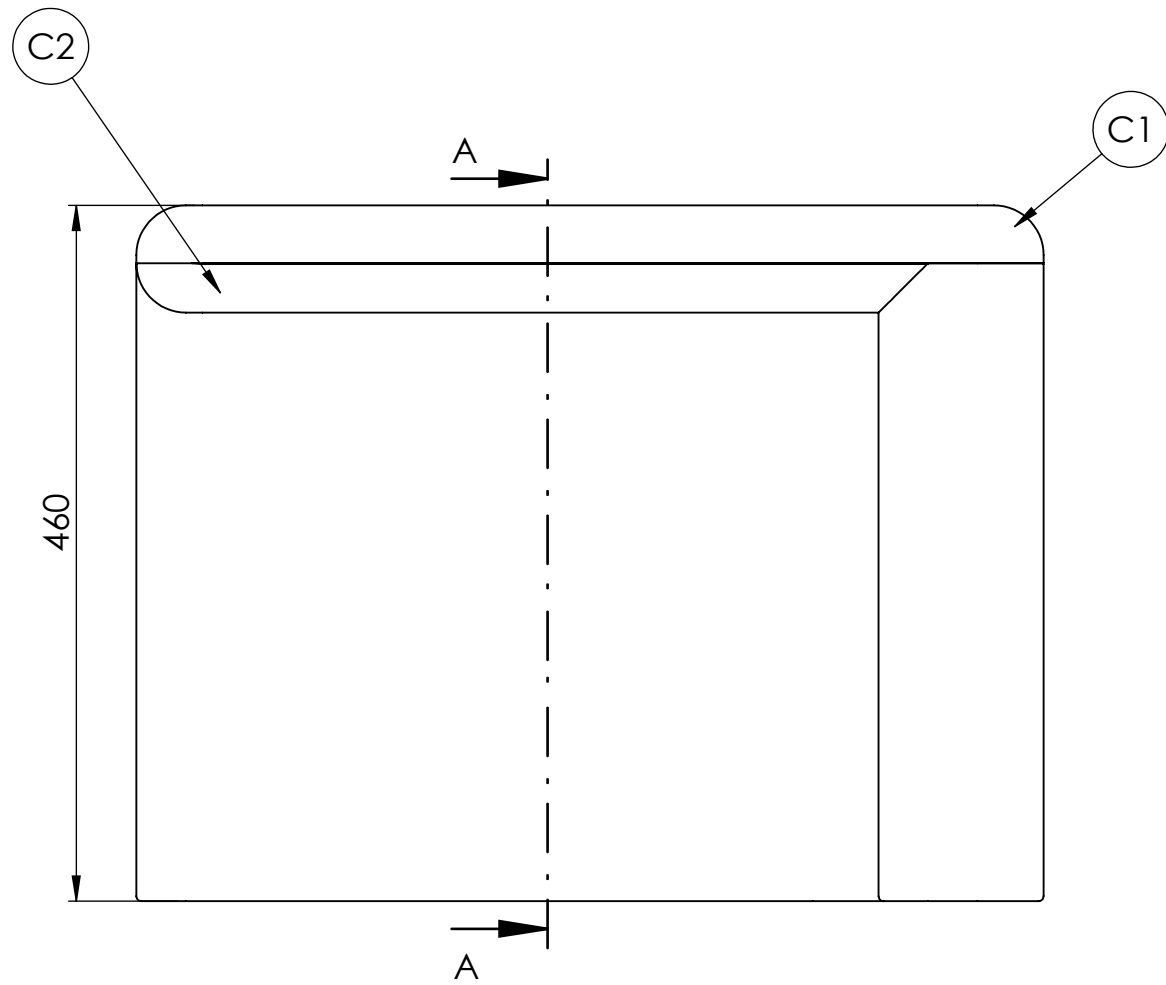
Detalle juntas para el ensamblaje (Fuente: propia)
